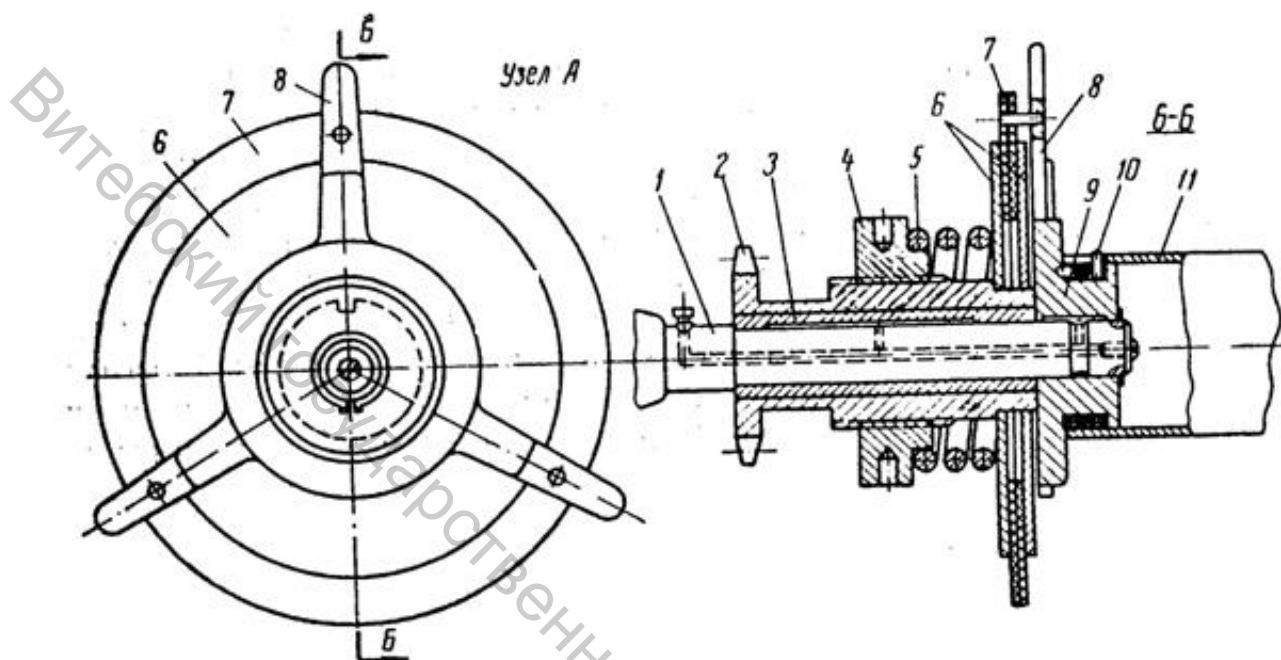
Схема фрикционной муфты товарного валика
